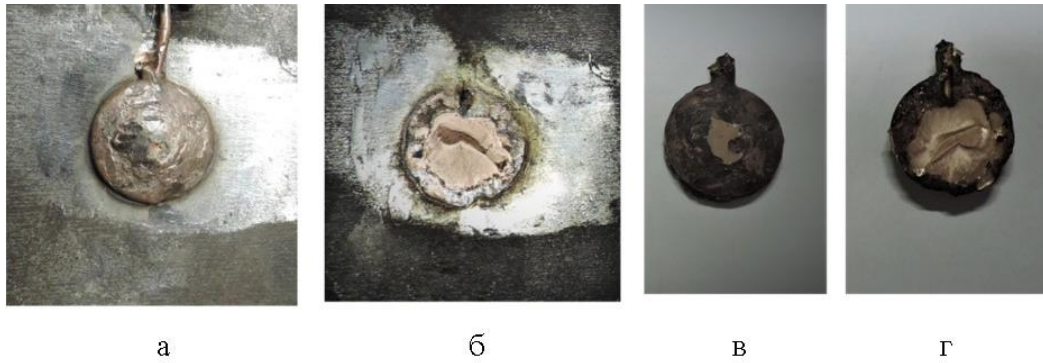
Внешний вид наплавки до (а) и после механического испытания на сдвиг (б - зона сплавления основного металла, в - лицевая сторона срезанной приварки, г - оборотная сторона срезанной приварки) образца К2
